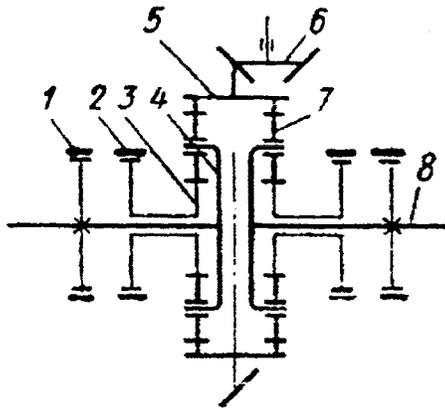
Схема механизма планетарного поворота трактора гусеничного: 1 – тормоз остановочный; 2 – тормоз шестерни солнечной; 3 – шестерня солнечная; 4 – водило; 5 – шестерня коронная; 6 – передача главная; 7 – сателлиты; 8 – вал заднего моста
